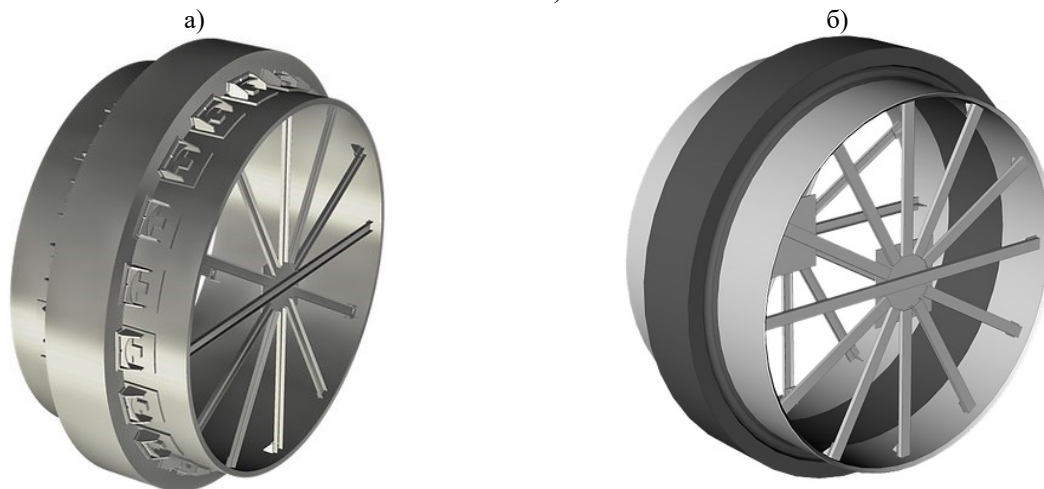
Основные типы применяемых бандажей [6]: а) плавающего типа, б) сварного типа
